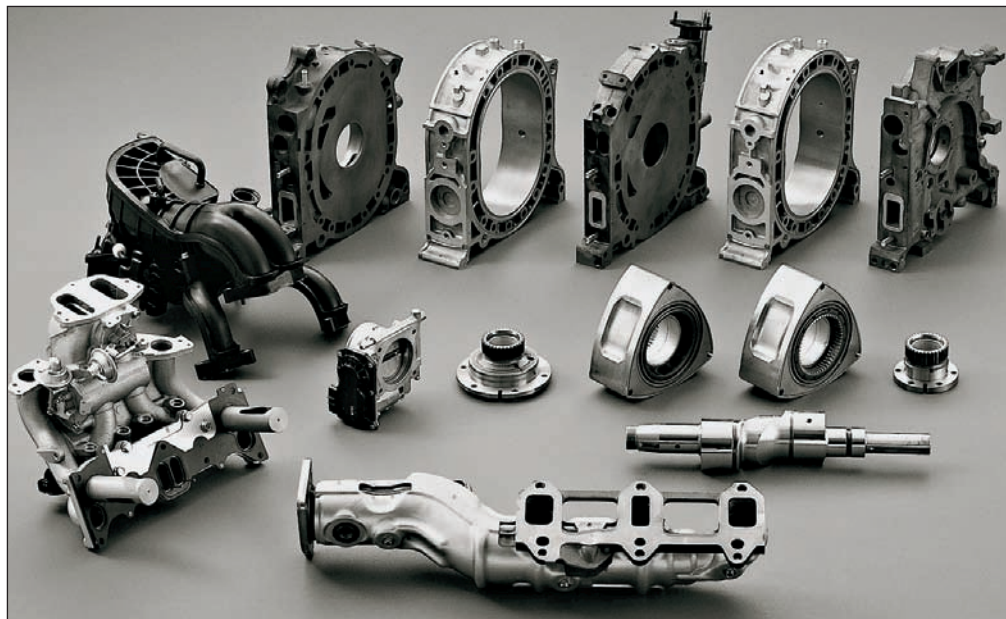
Детали двухроторного двигателя автомобиля Mazda
